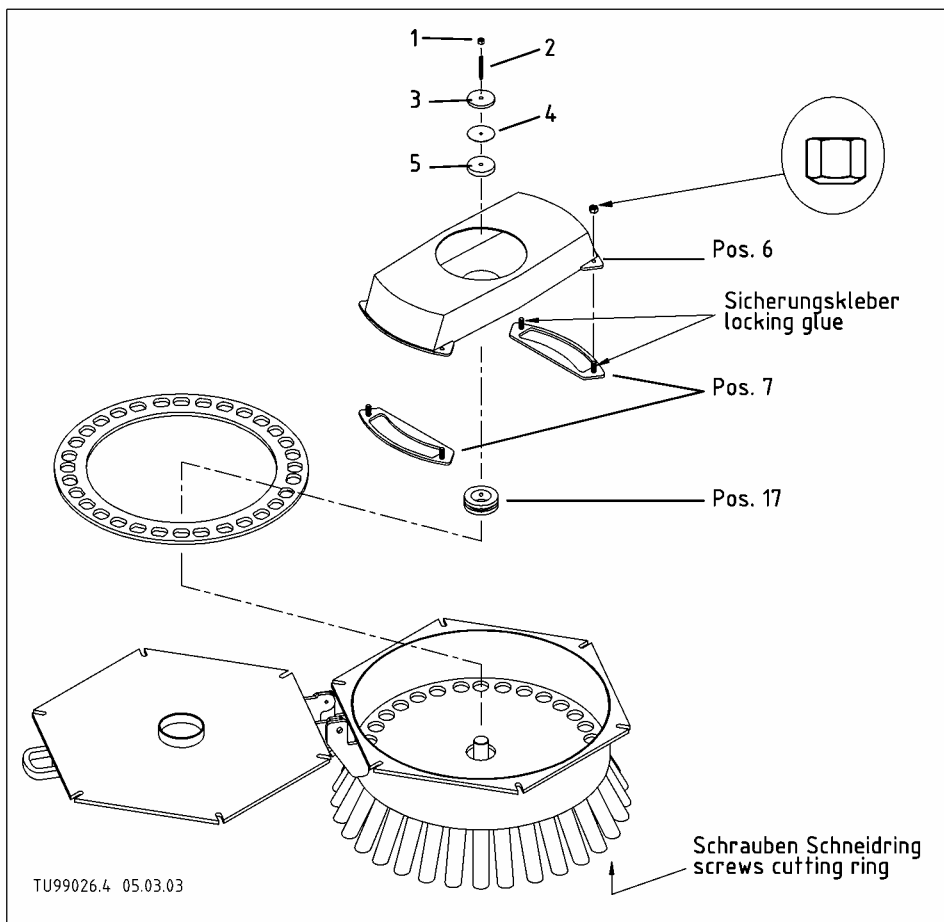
Austausch der Verschleißteile / Fig. 5.4 Replacement of wear parts
